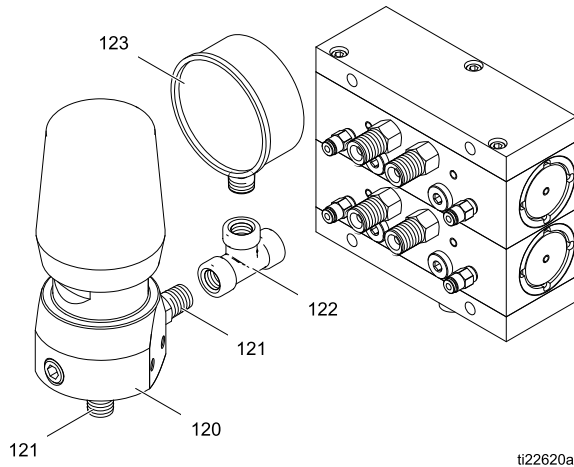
Installation eines Gegendruckreglers am Ablassventil des Auslass-Ventilblocks
